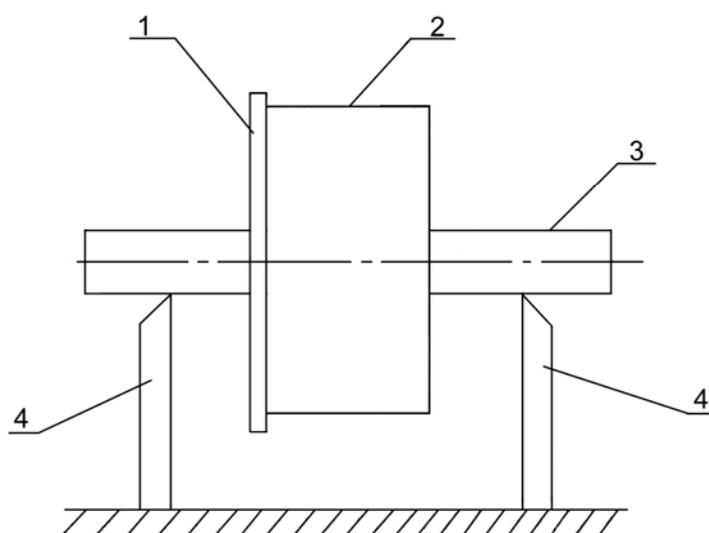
Схема установки рабочего колеса вентилятора при балансировке:
